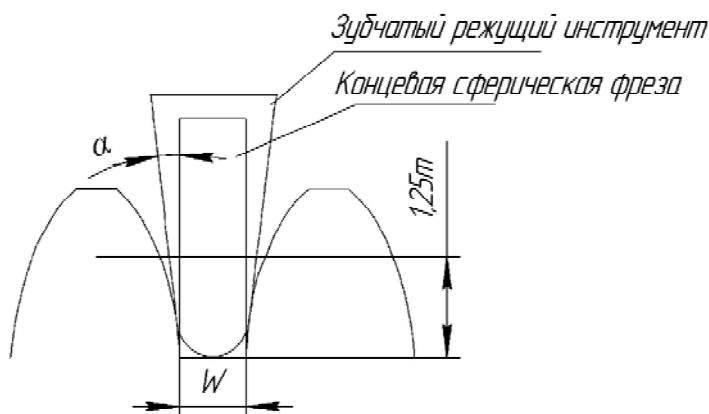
Соотношение концевой фрезы и зубчатого режущего инструмента
